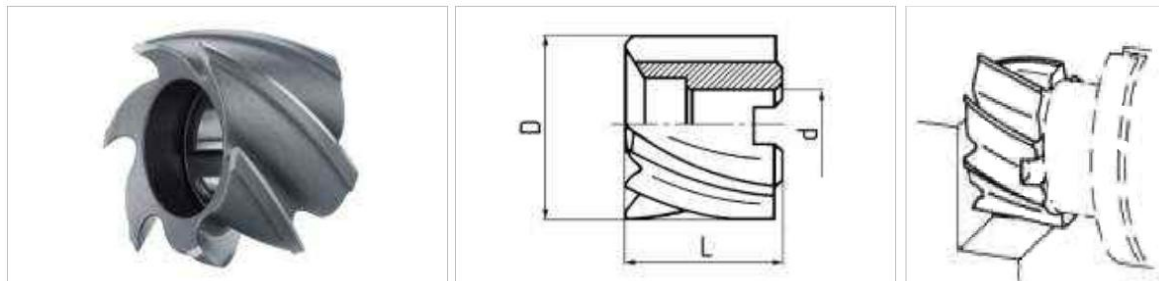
Fréza válcová čelní – Morse kužel [23].
